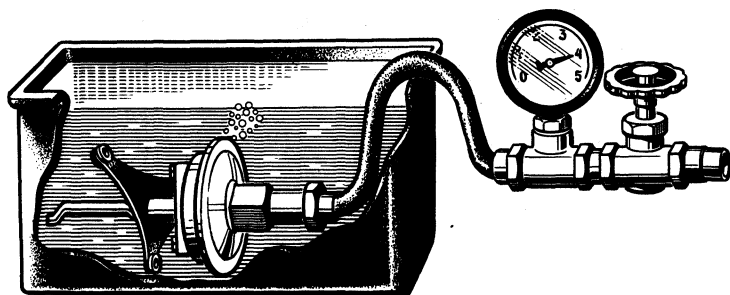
Проверка герметичности вакуумного регулятора прерывателя-распределителя
